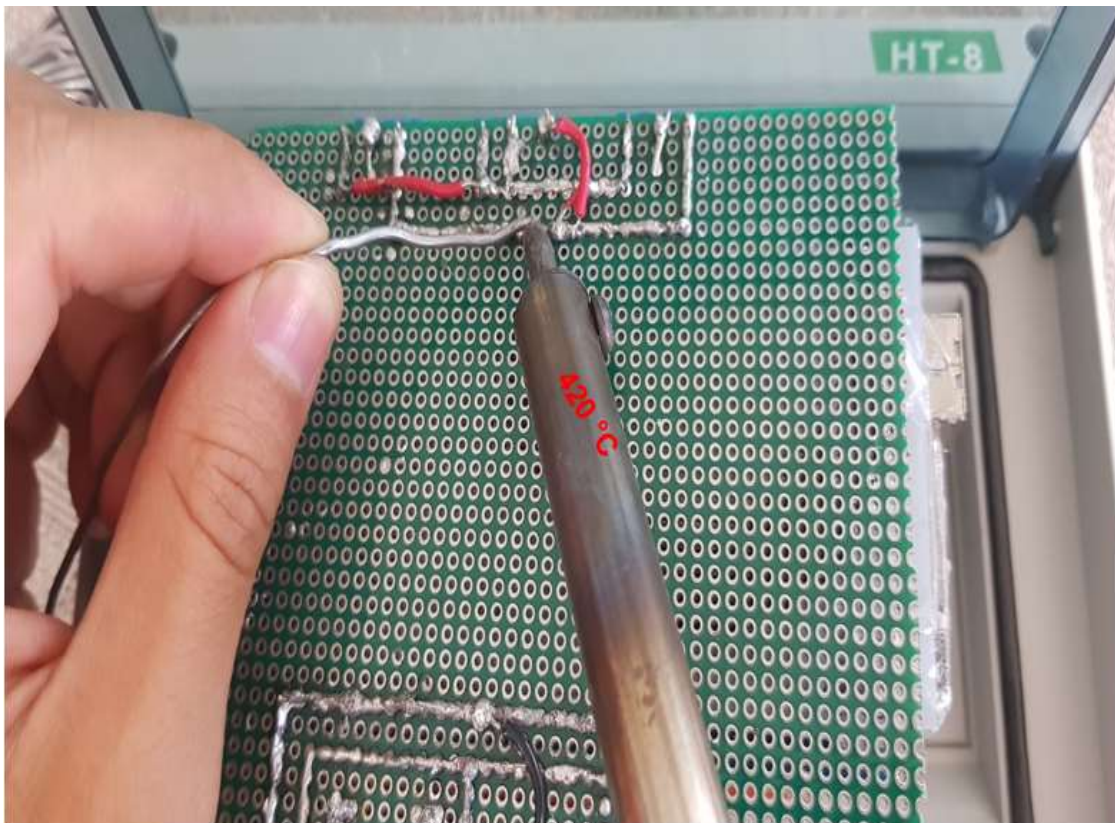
Elaboración y soldado de pistas de la placa
